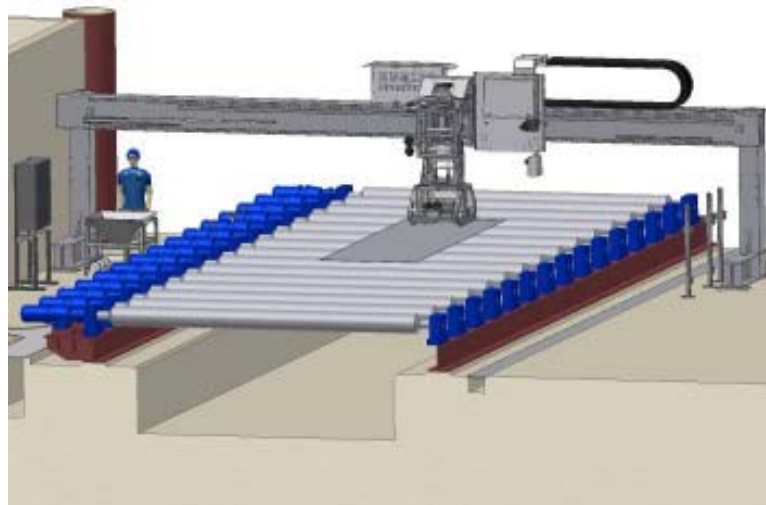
Versione a ponte di una macchina di marcatura multi ugello
